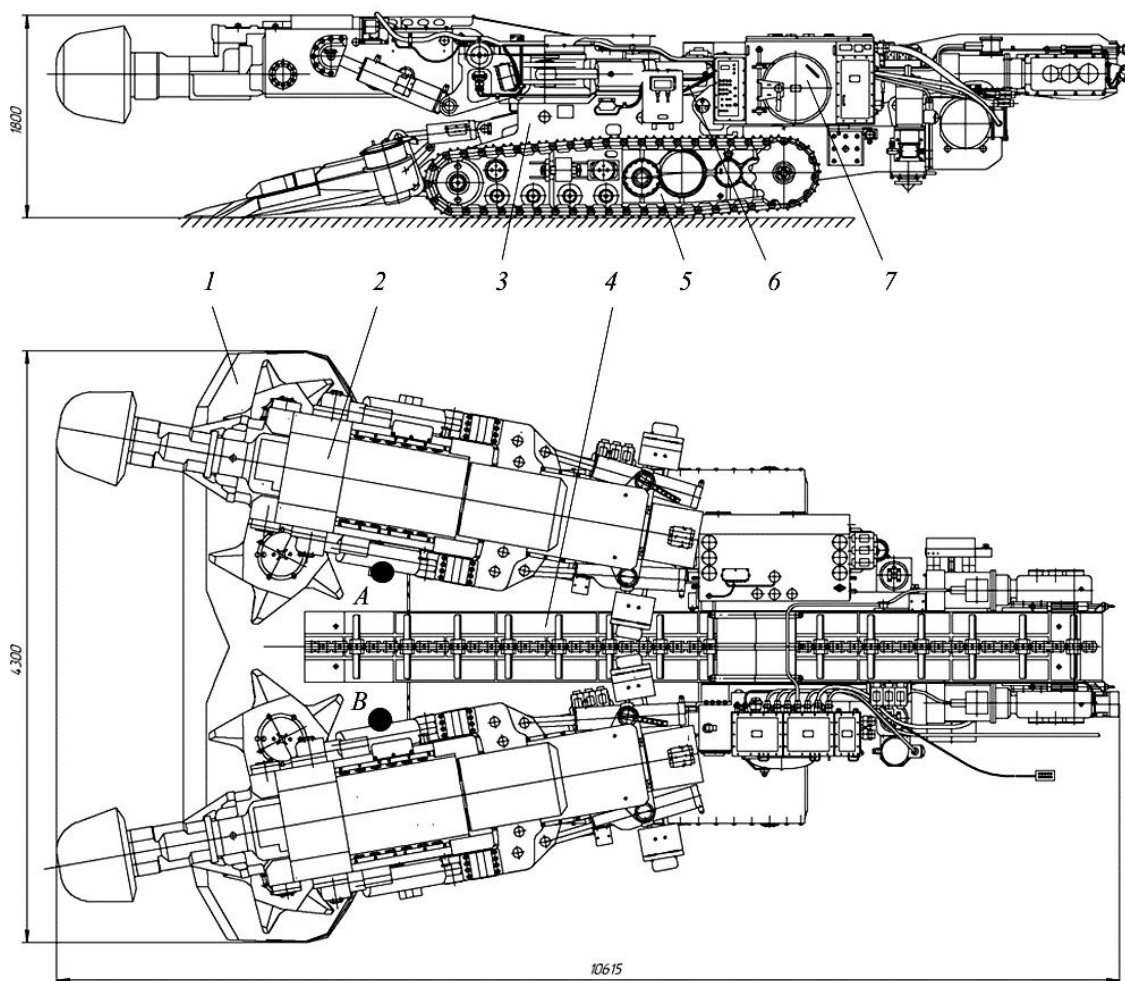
Общий вид проходческого комбайна с двумя исполнительными органами
